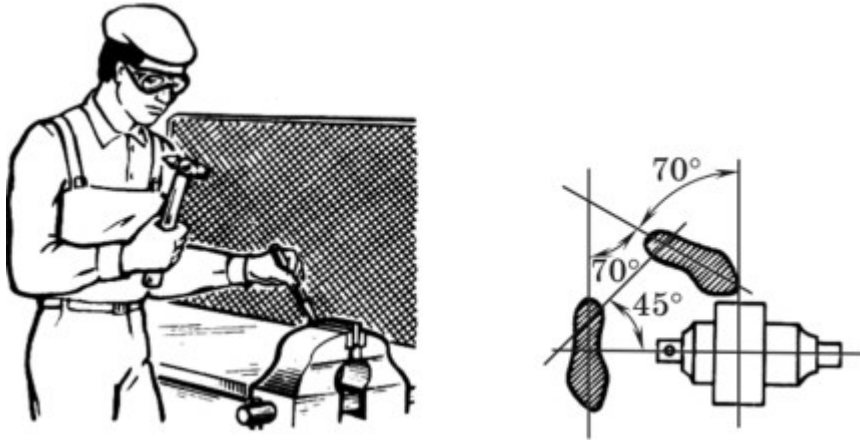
Положение корпуса и ног при рубке зубилом
